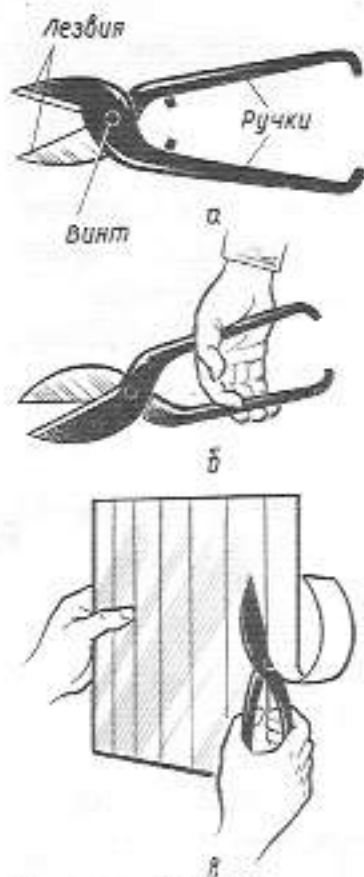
Ножницы по металлу: а — устройство; б — захват ножниц; в — работа ножницами.
